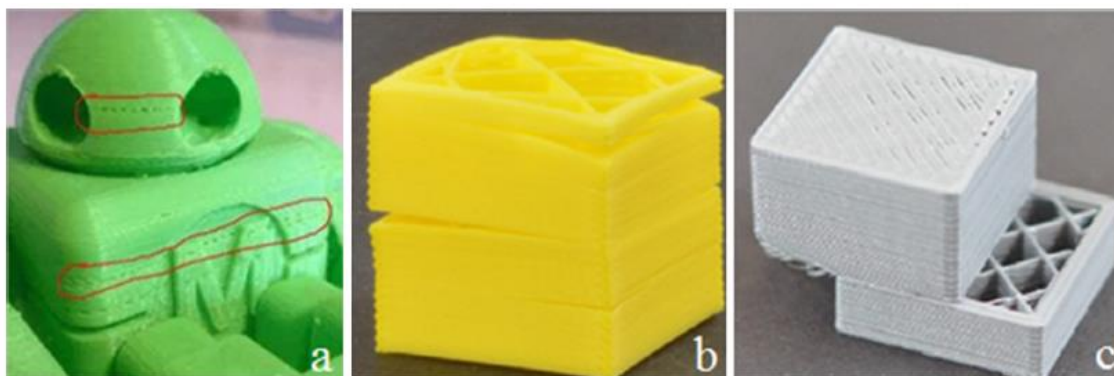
a) Infill Visível no exterior da peça; b) Camadas em falta; c) Camadas Desalinhadas (8).
